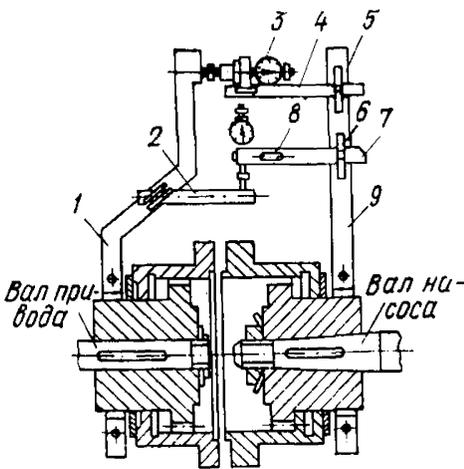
Приспособление для центровки насосов и приводов по полумуфтам
